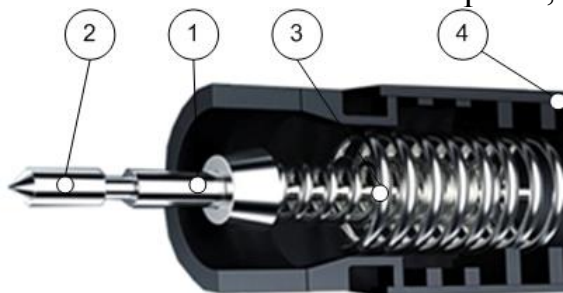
Механизм стеклобоя нажимного типа: 1- металлический стержень; 2 – боёк; 3 – пружины; 4 - корпус
